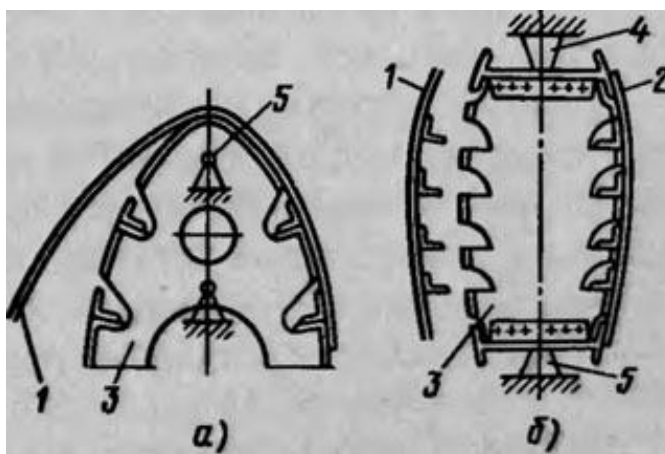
Схема сборки по базе «внутренняя поверхность обшивки»: 1, 2 – обшивки; 3 – макетная нервюра; 4, 5 – фиксаторы приспособления
